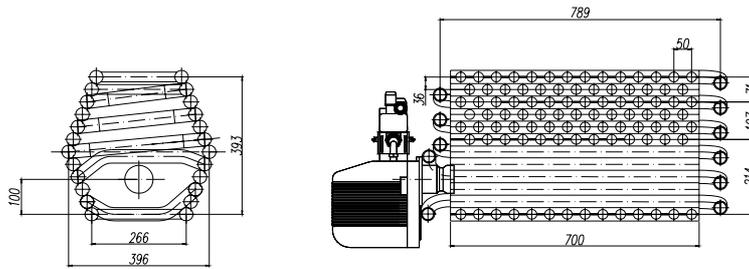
Расположение поверхности нагрева в трехходовой конструкции
